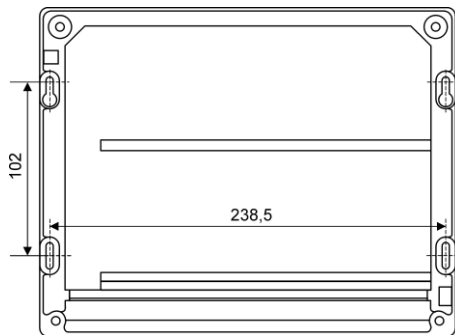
Присоединительные размеры составной части контроллера в корпусном исполнении
